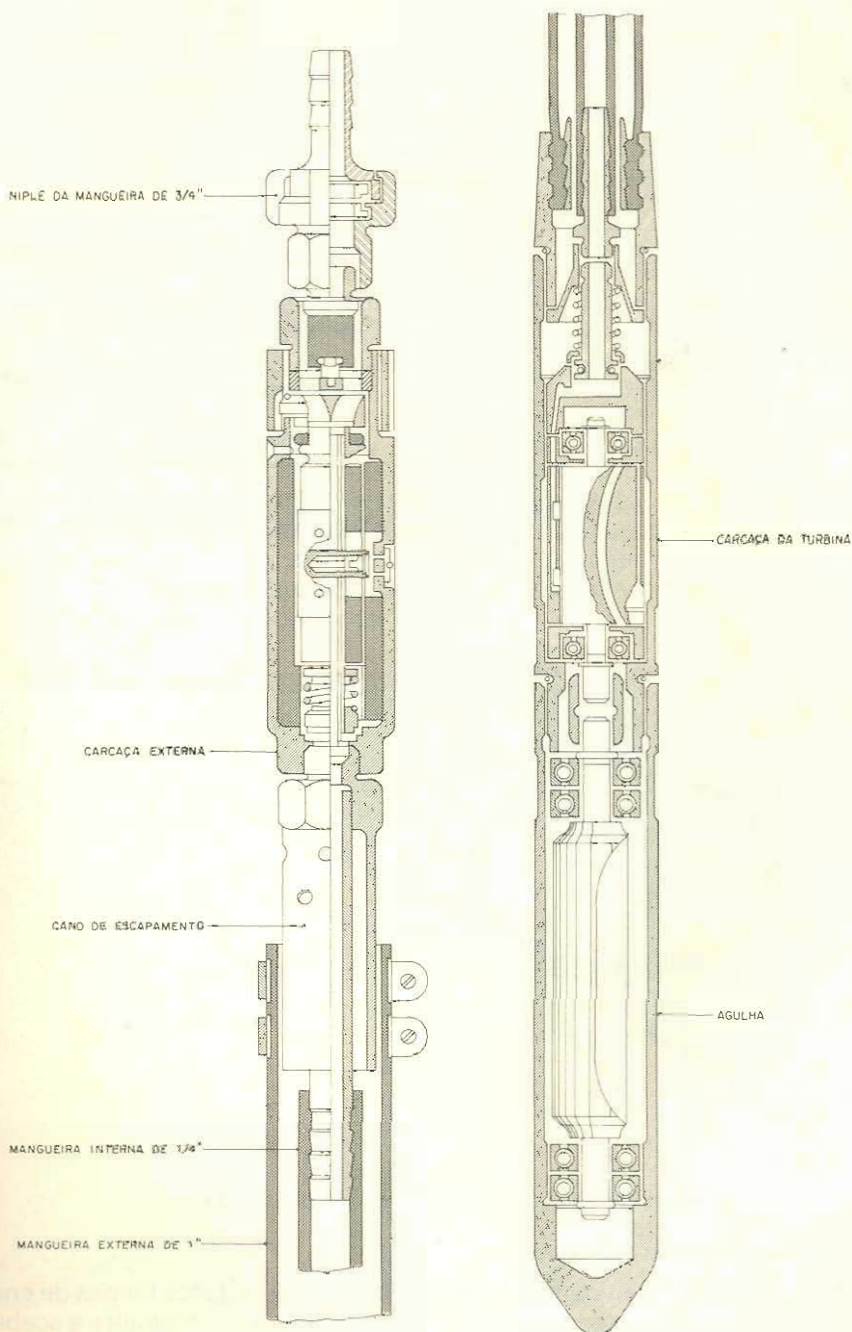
Detalhe dos vibradores da Figura 12.25
